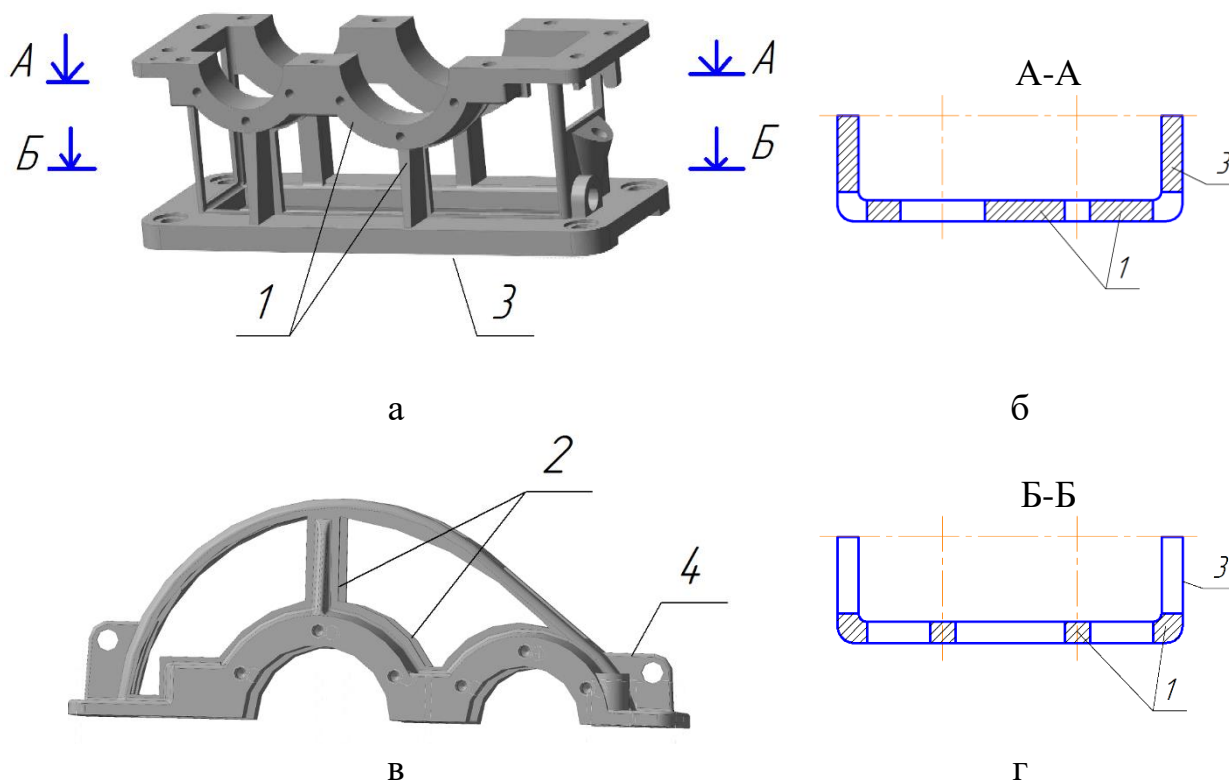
Полегшена металева конструкція одноступінчастого редуктора:
